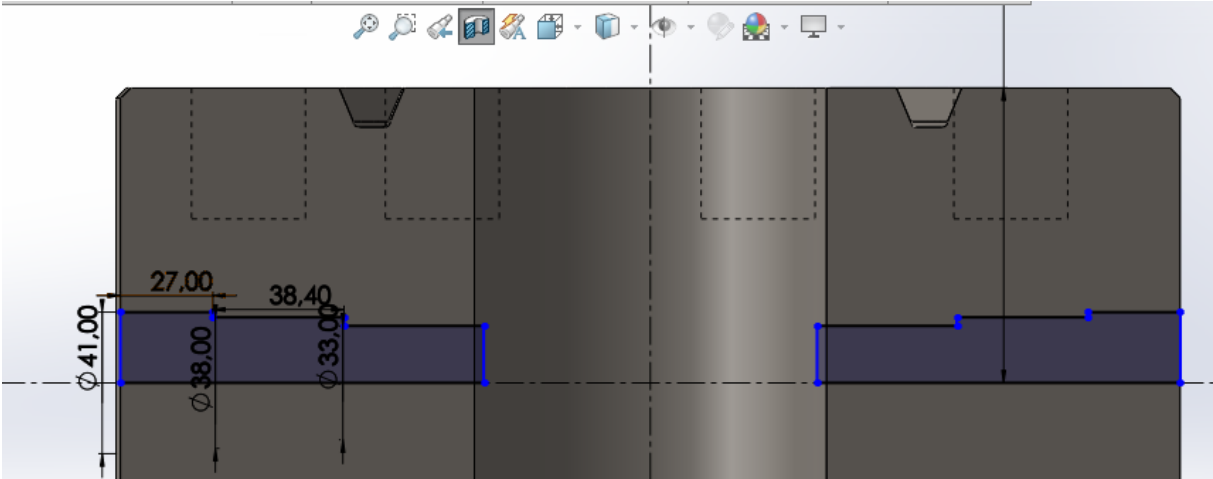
Dimensionnement des trous de passage des pointeaux
